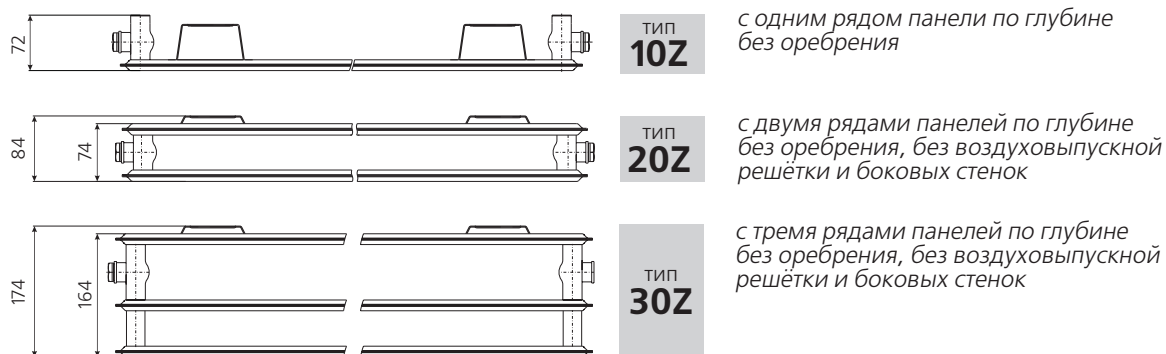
Радиатор «PRADO Universal Z» в разрезе, с двумя нижними и четырьмя боковыми присоединительными отверстиями
